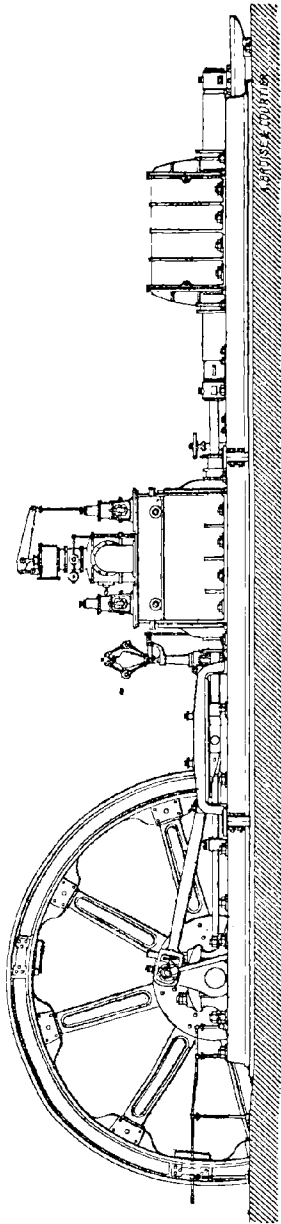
Machine soufflante horizontale de Rimamarany-Salgo-Torjaner (élévation).
